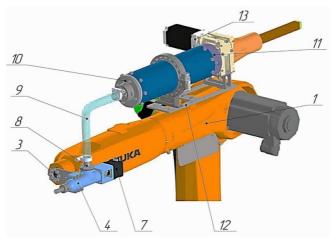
Устройство для 3D-печати строительными смесями на основе вяжущих: 1 - робот-манипулятор, 3 — фланец, 4 — экструдер, 7 — шаговый двигатель, 8 — штуцер, 9 — гибкий шланг, 10 — переходная втулка, 11 — нагнетатель, 13 — мотор-редуктор.
